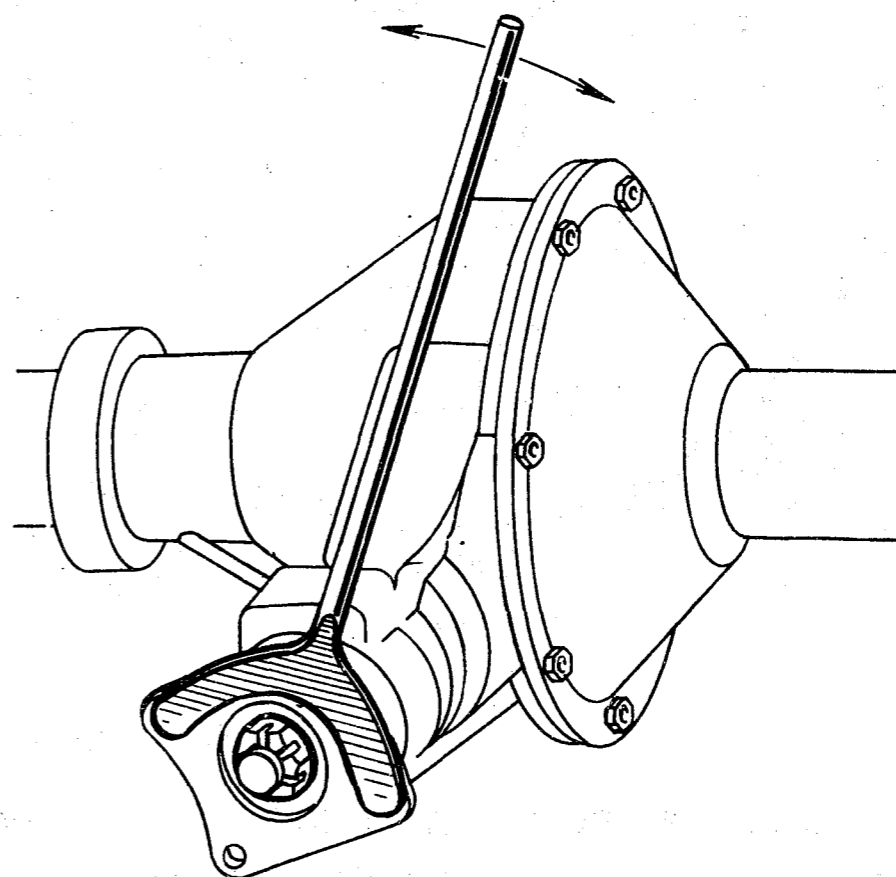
Удерживание фланца вилкой 78II-46I2 при затягивании гайки ведущей шестерни
